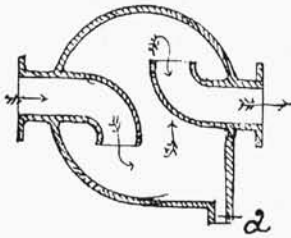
wyobraża jeszcze jeden typ odwodniacza, budowanego przez tę samą fabrykę J. Losenhausen. Para, jak to wskazują strzałki, schodzi najpierw na dół przyrządu, omija pierwszą ściankę, podnosi się znowu do góry i tam przechodzi przez otwór zrobiony w drugiej ściance i t. d. Otwory te posiadają w kierunku ruchu pary daszki, w celu nadania parze kierunku więcej łamanego. Przyrząd ten, chociaż, jak głosi fabryczna reklama, rozpowszechnił się w tysiącach egzemplarzy, mało wzbudza zaufania, gdyż posiada dość dużą powierzchnię ścianek rozdzielczych, co przyczynia się bezwarunkowo do kondensacji pary tembardziej, że posiada przyrząd ten dość znaczne martwe przestrzenie, jak przestrzeń *A* i *B*, w których para znajduje się we względnym spokoju. Przytem przyrząd ten nie jest wolnym od wady tak często spotykanej w odwodniaczach, t. j. że para przecina ściekającą wodę wydzieloną.
